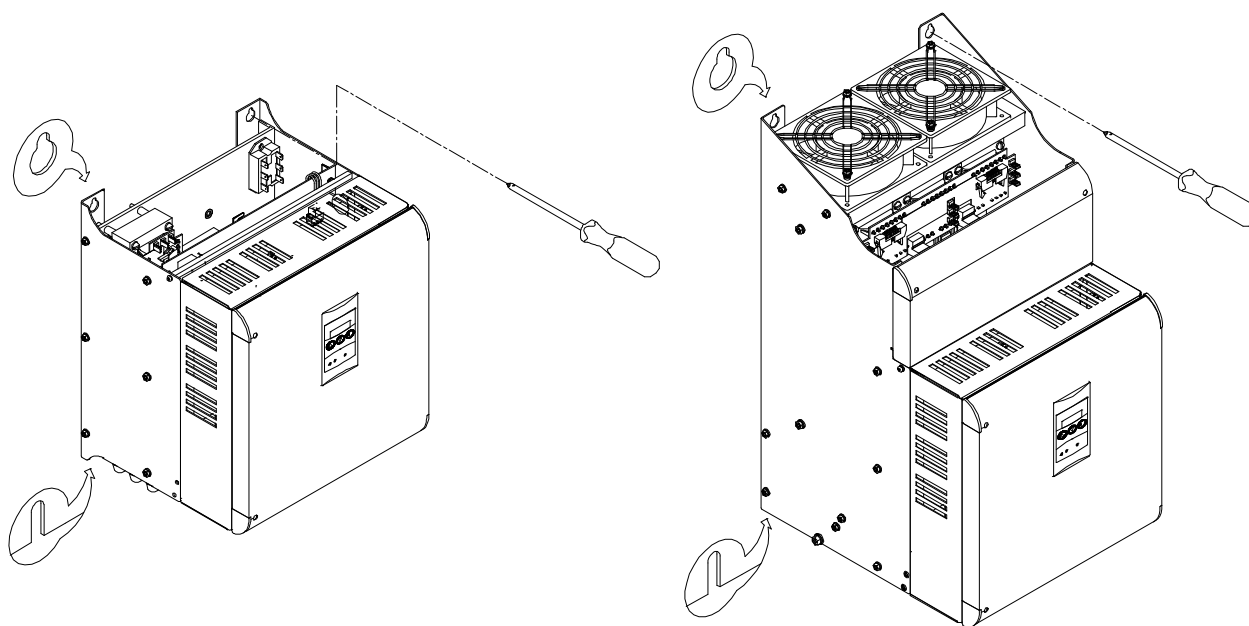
Procedimento de Instalação do CTW-04 em Superfície
